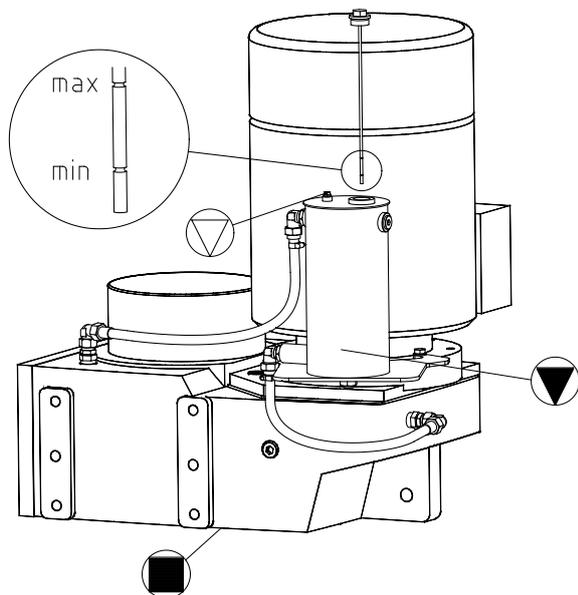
Редукторы с параллельными валами и маслоизмерительным бачком
